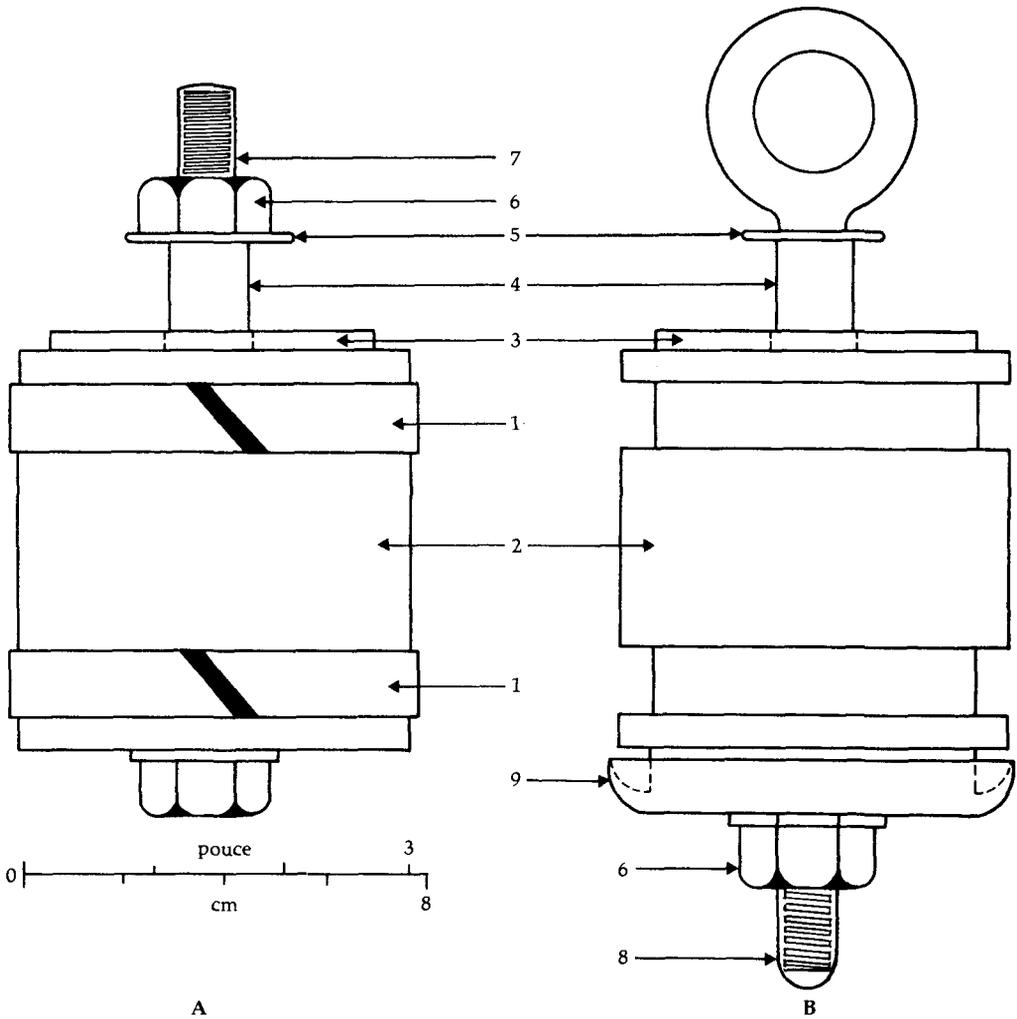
(A) Piston et (B) assemblage du clapet de pied de la pompe à main Waterloo : 1) rondelle de polyéthylène ; 2) piston ; 3) soupape à plaques en PVC ; 4) guide de soupape en laiton ; 5) rondelle plate ; 6) écrou ; 7) boulon ; 8) boulon à œil ; et 9) adaptateur de clapet de pied en polyéthylène.
